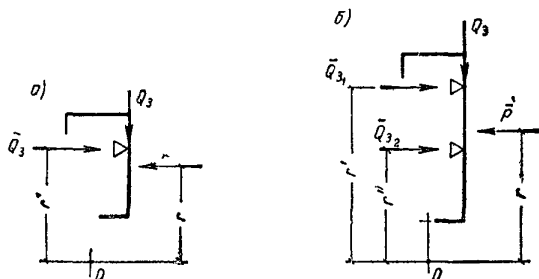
Схемы для определения расчетных нагрузок на замки
